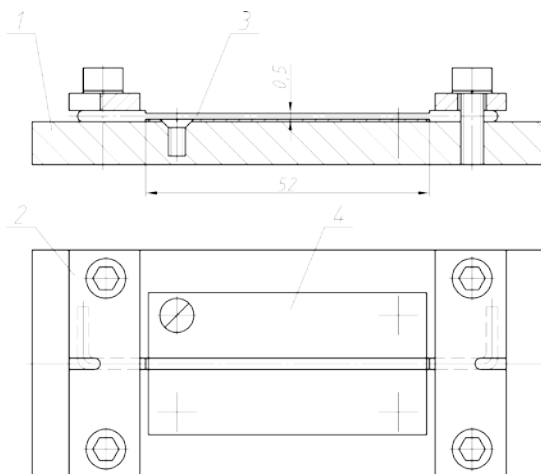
Схема технологической оснастки для изготовления образцов
